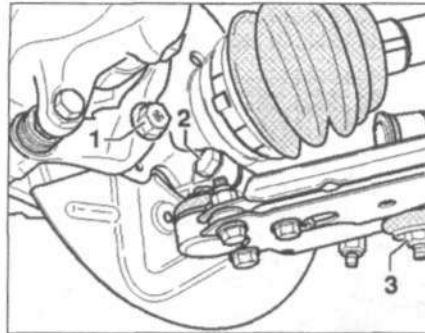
Открутите болт 1 крепления опоры тормозного суппорта и болт 2 из поворотного кулака. Открутите гайку 3 крепления соединительной тяги стабилизатора поперечной устойчивости.
